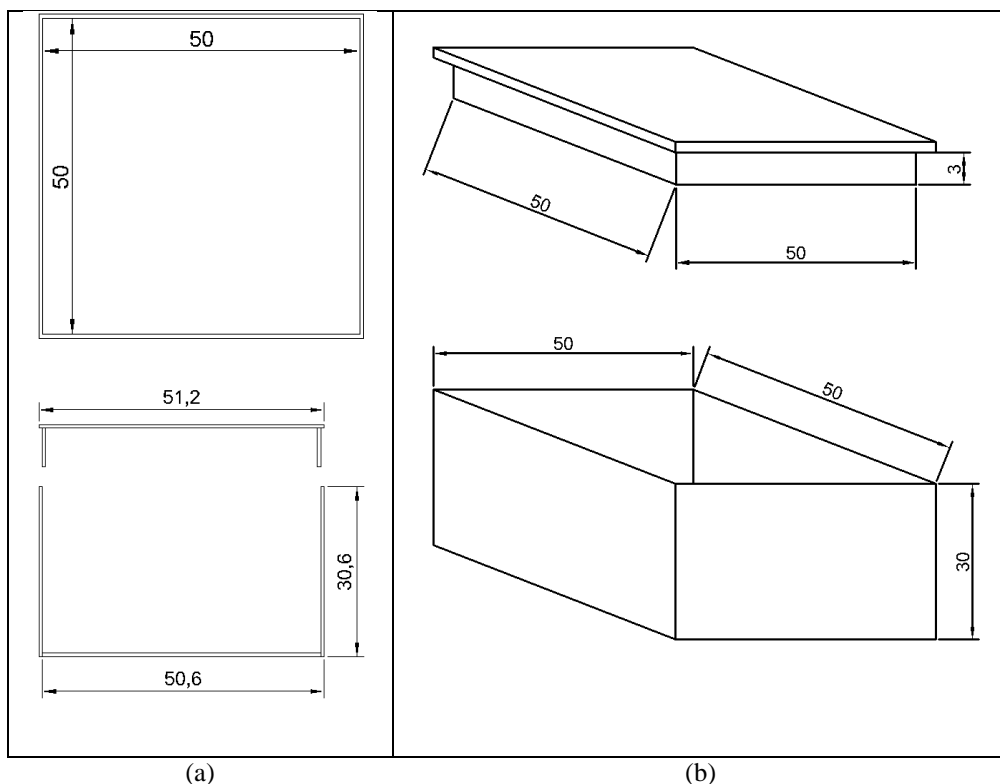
Dimensões da caixa, (a) em planta e (b) em perspectiva
